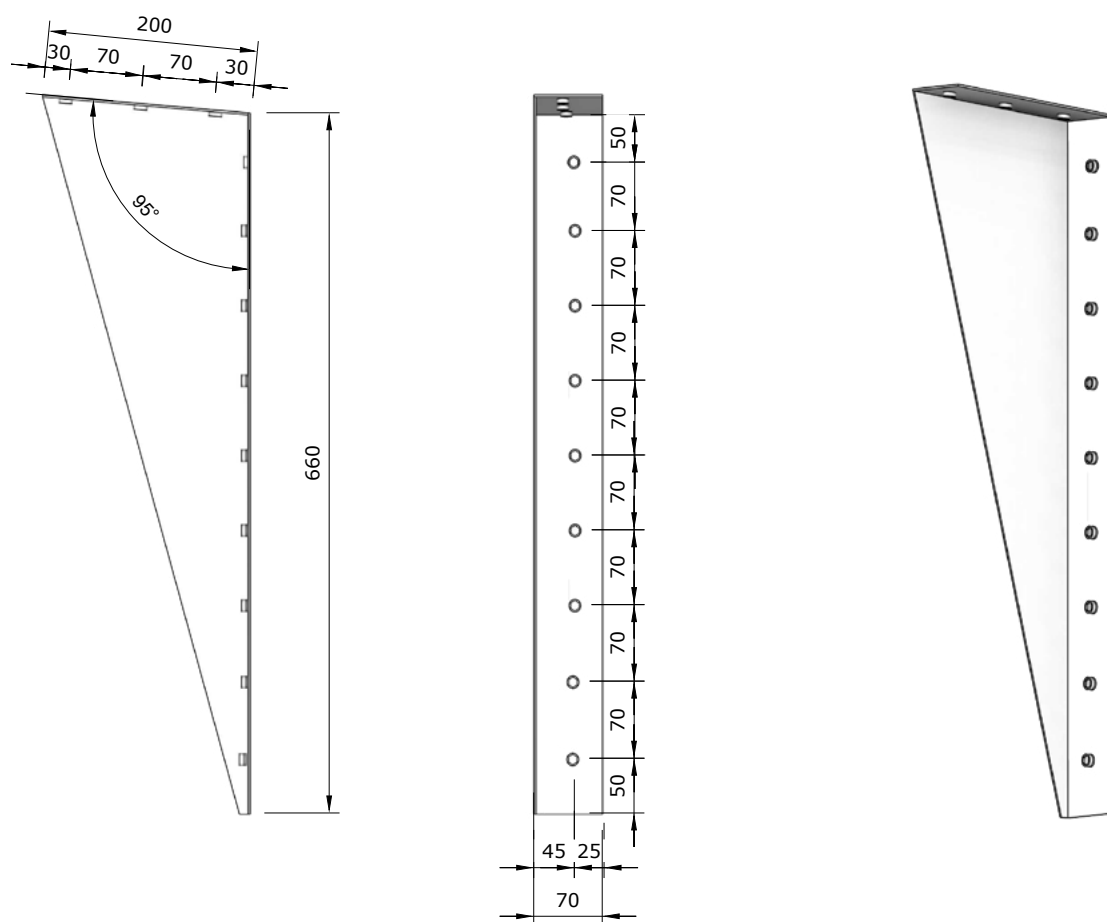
Vues de la tôle de support avec les dimensions de la fixation, dimensions en mm.
